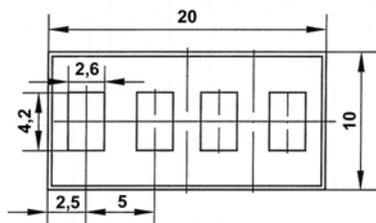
Внешний вид и габаритные размеры индикатора ИПВ72А-4/5х7Л
